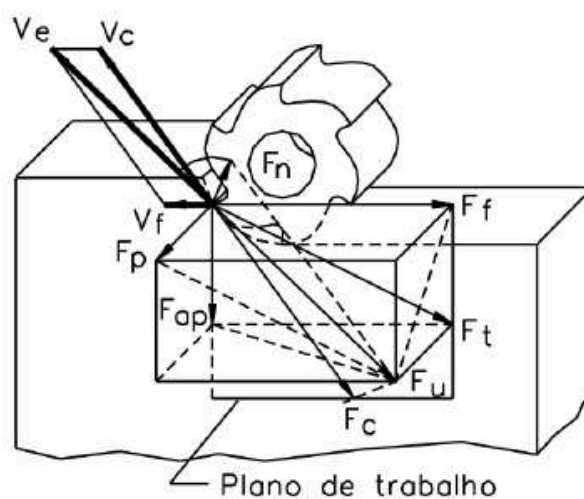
Força de usinagem e seus componentes para os processos de fresamento (MACHADO; SILVA, 2004).
